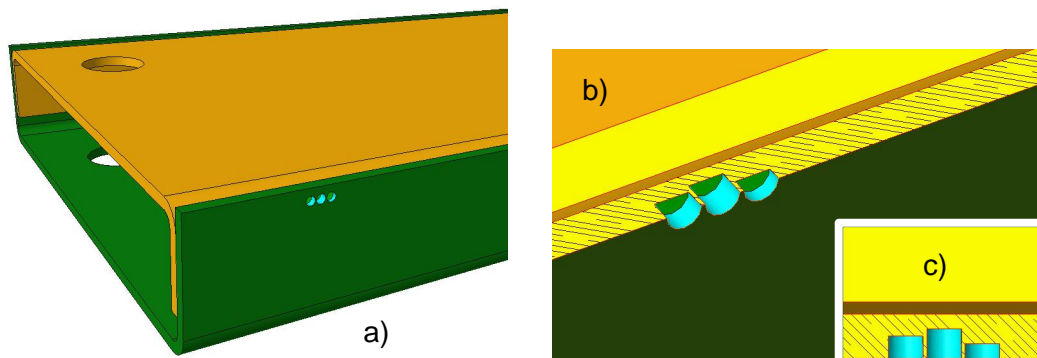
Preparación para instalación de termopares en la pieza de trabajo, a) Vista en perspectiva de perforaciones; b) Corte longitudinal en el plano horizontal en isométrico; c) Corte longitudinal en el plano horizontal vista superior.
